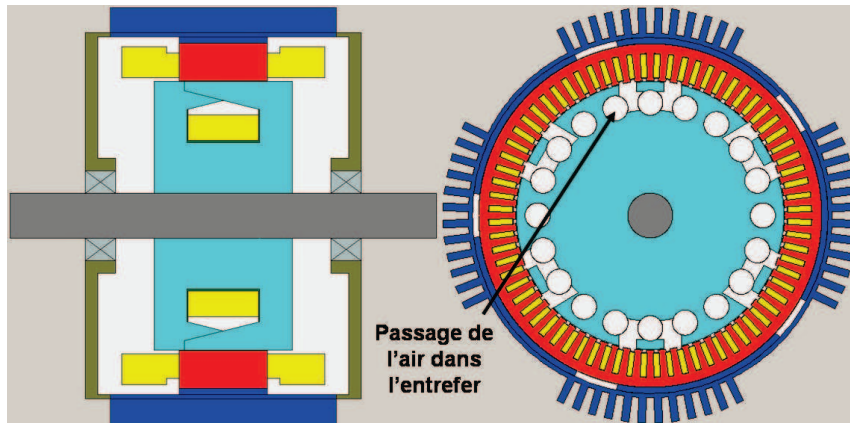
Vues du modèle de la machine à griffes développé sur Motorcad
